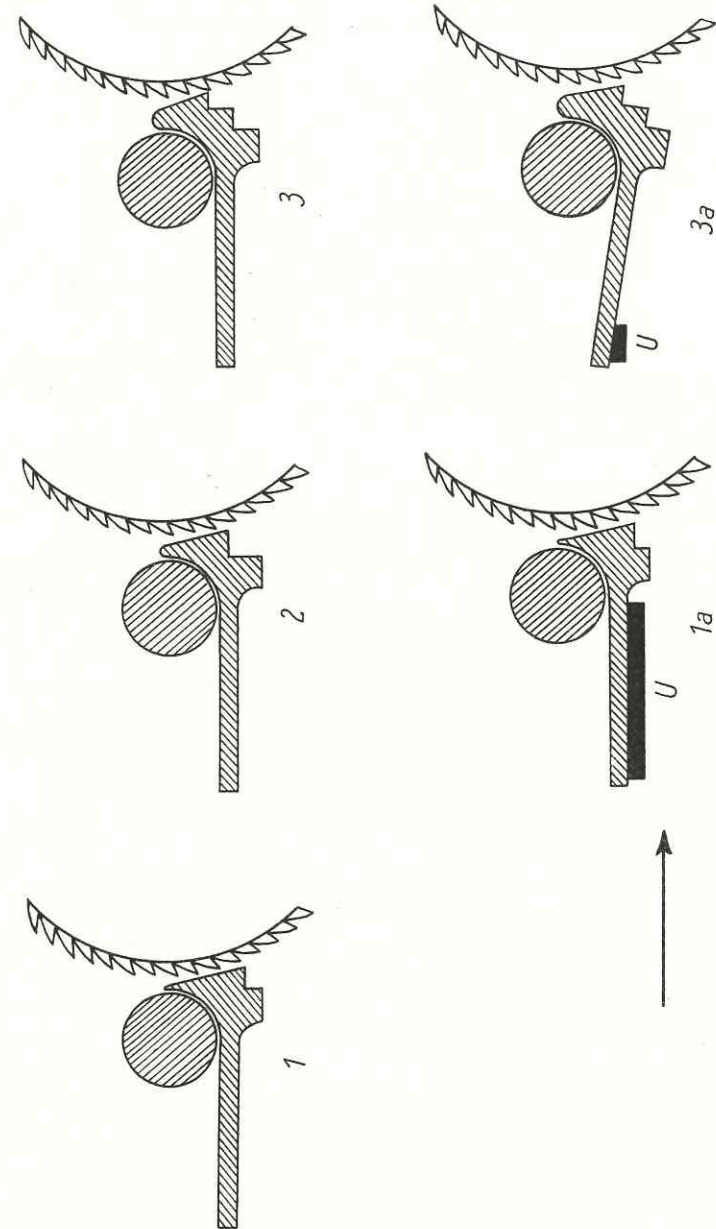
Muldenform des Einzugsstisches an der Baumwollkarde, Umstellung auf Vistrafaser 60–70 mm Schnittlänge
